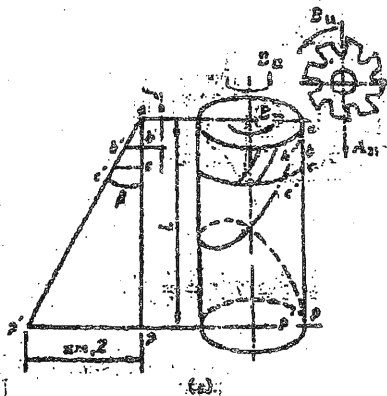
滚切斜齿圆柱齿轮的传动原理图
